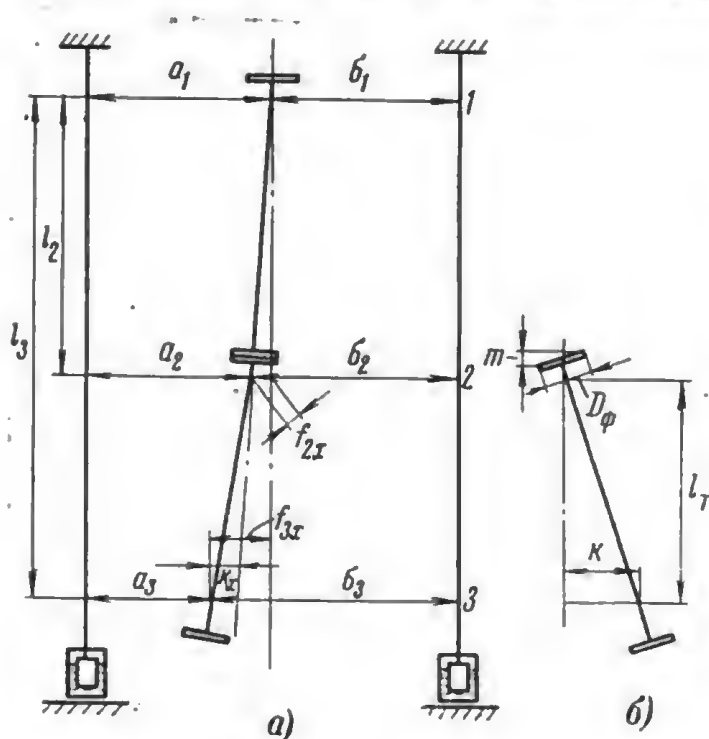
Схема центровки турбины с промежуточным валом.
